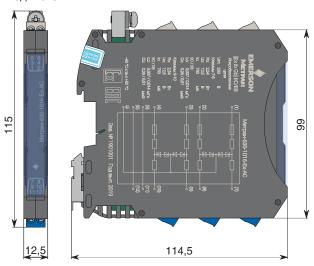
Габаритные размеры барьера с разъемами с винтовыми клеммниками
